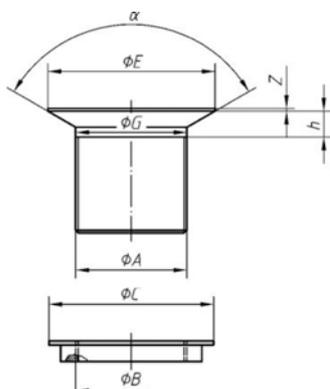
Ablaufventil ohne Überlaufanschluss, mit Mutter
